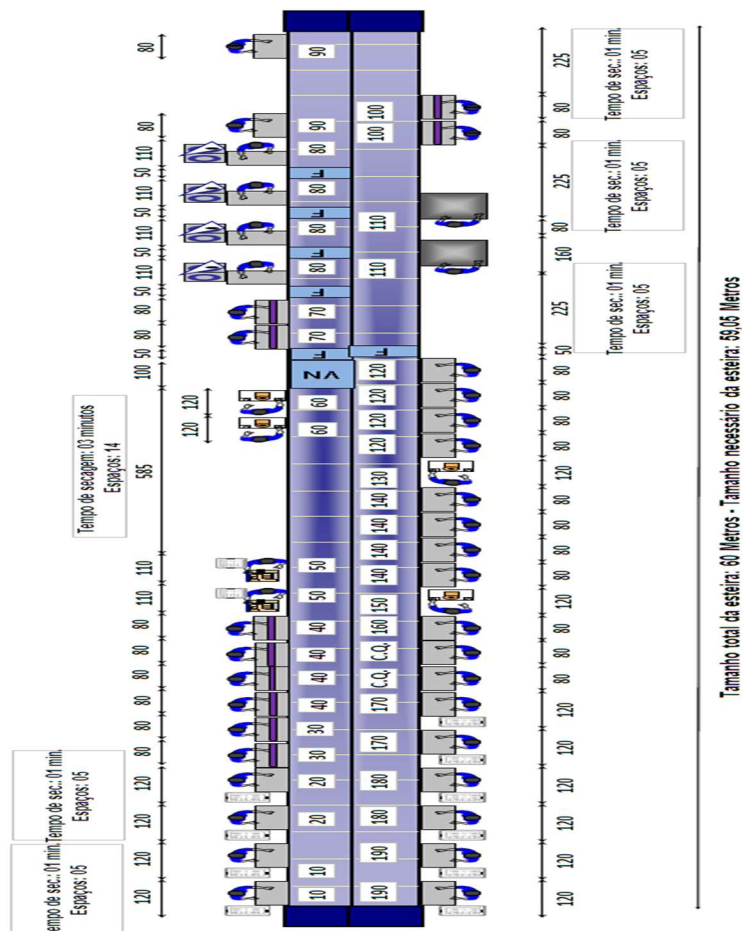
Layout proposto da linha de montagem. Fonte: Engenharia da empresa.
